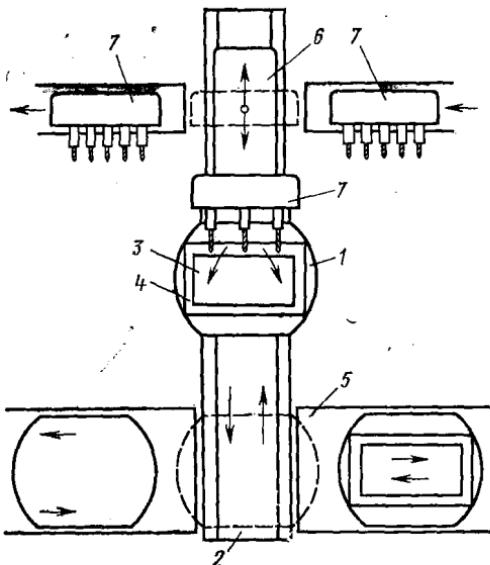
Станочная система с ЧПУ и смен-ными шпиндельными коробками для много-инструментной обработки
